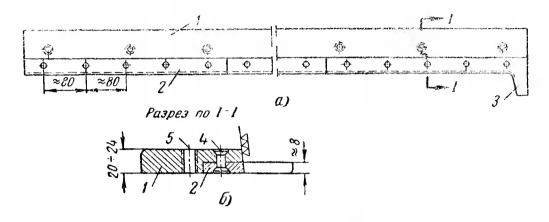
Верхний нож к гильотинным ножницам. а — общий вид; б — разрез ножа; I — основание; 2 — вставка из инструментальной стали; 3 — предохранительный выступ; 4 — заклепка; 5 — отверстие для крепления.
